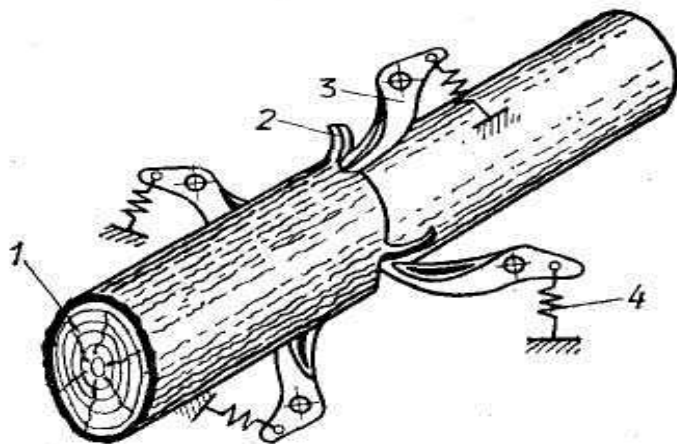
Общий вид окорочного станка роторного типа ОК63-1:
